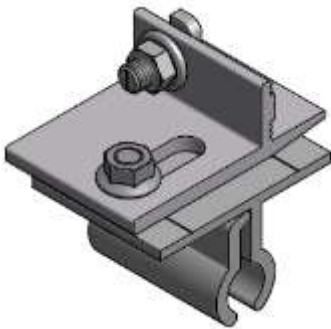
KalZip®-Klemme mit Universalverbinder
